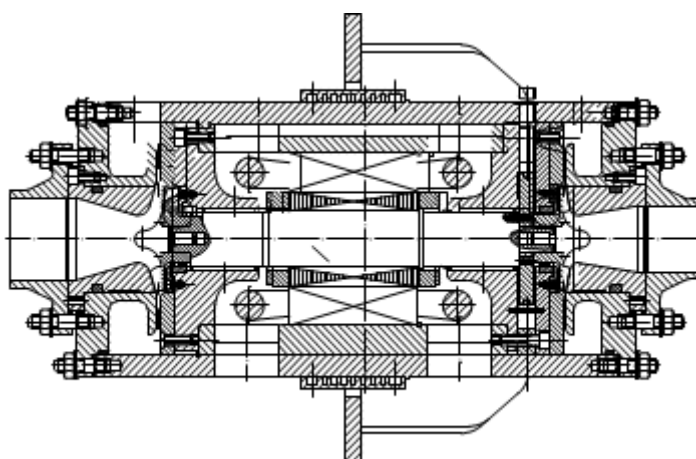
б. Двухступенчатый холодильный центробежный компрессор со встроенным электродвигателем и газодинамическими подшипниками (ВНИИХолодмашхолдинг, г. Москва)
